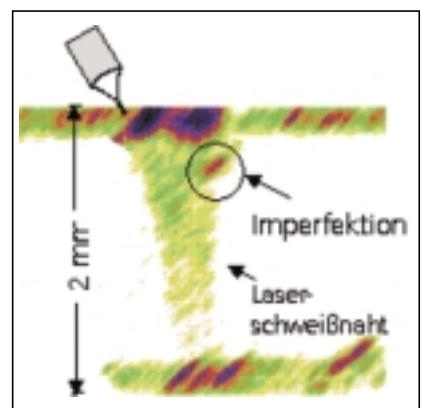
Hochauflösende Fokusprüfung einer Imperfektion in einer 2 mm dicken Laserschweißnaht – Seitenansicht
